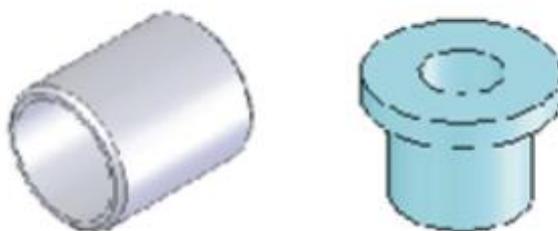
Направляющие детали. Кондукторные втулки.
